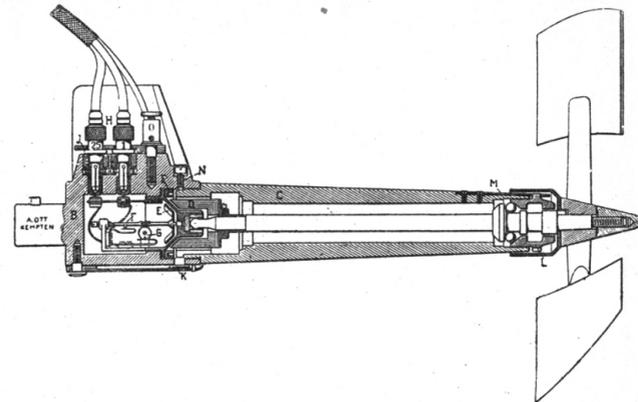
Detalle del contacto en cámara hermética. D, iman en forma de campana. E, ancla, F, contacto de vuelta en vuelta; G, rueda de 25 dientes para contacto cada 25 vueltas.
